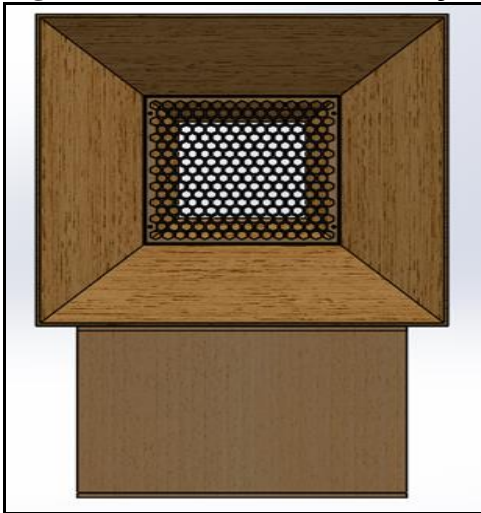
Túnel de vento dimensionado no *SolidWorks
